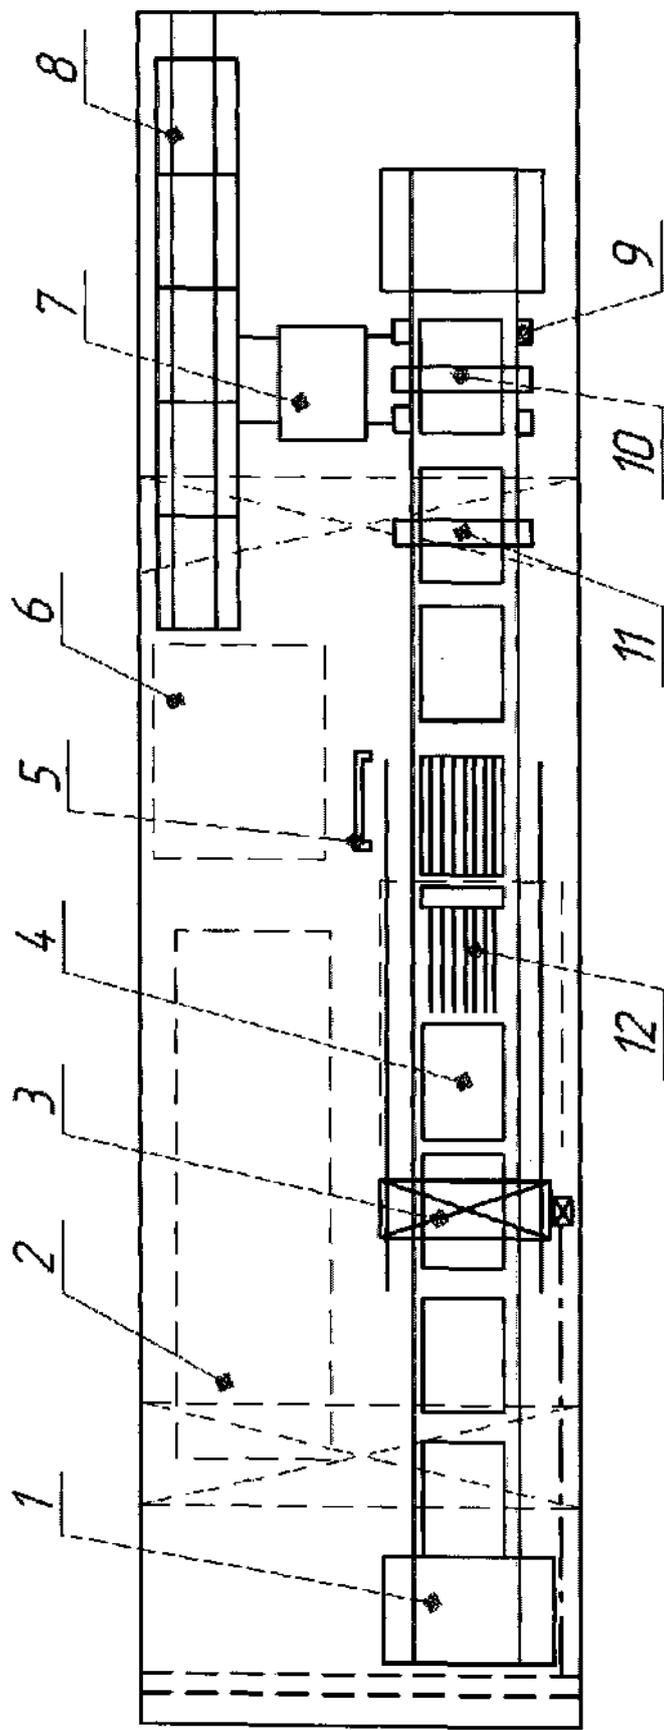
Конвейерная линия по производству многослойных плит перекрытия.
